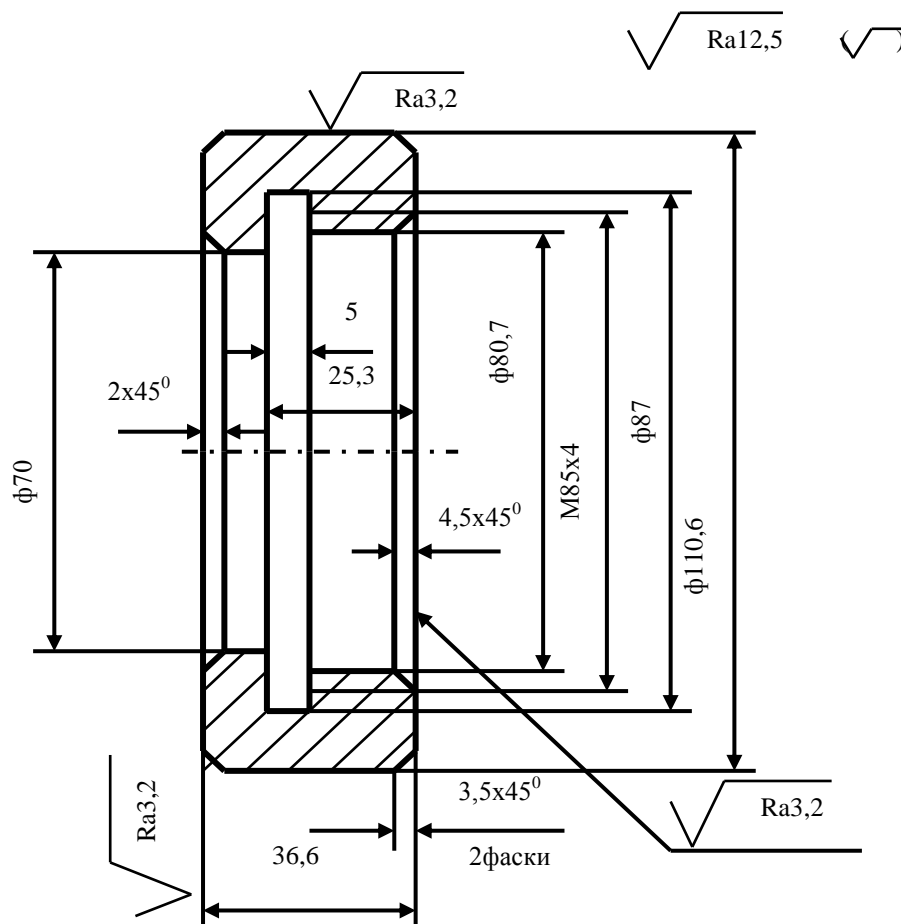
Чертеж токарной заготовки (оформляется на формате А4)
